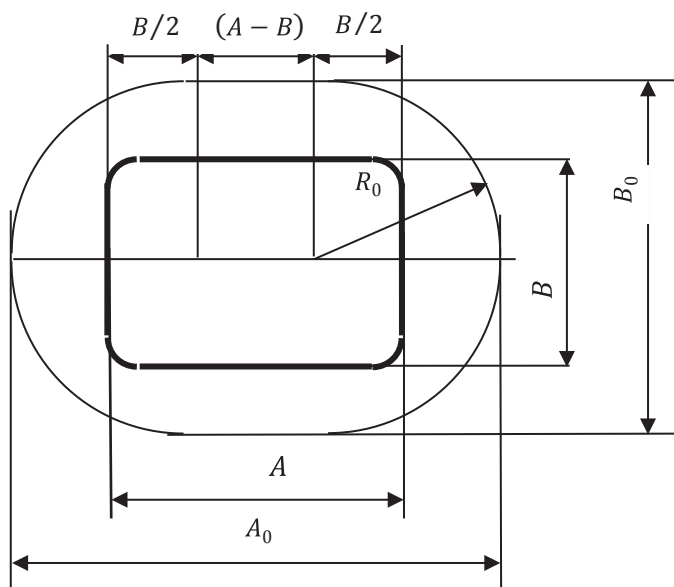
Заготовка для прямоугольных высоких деталей
